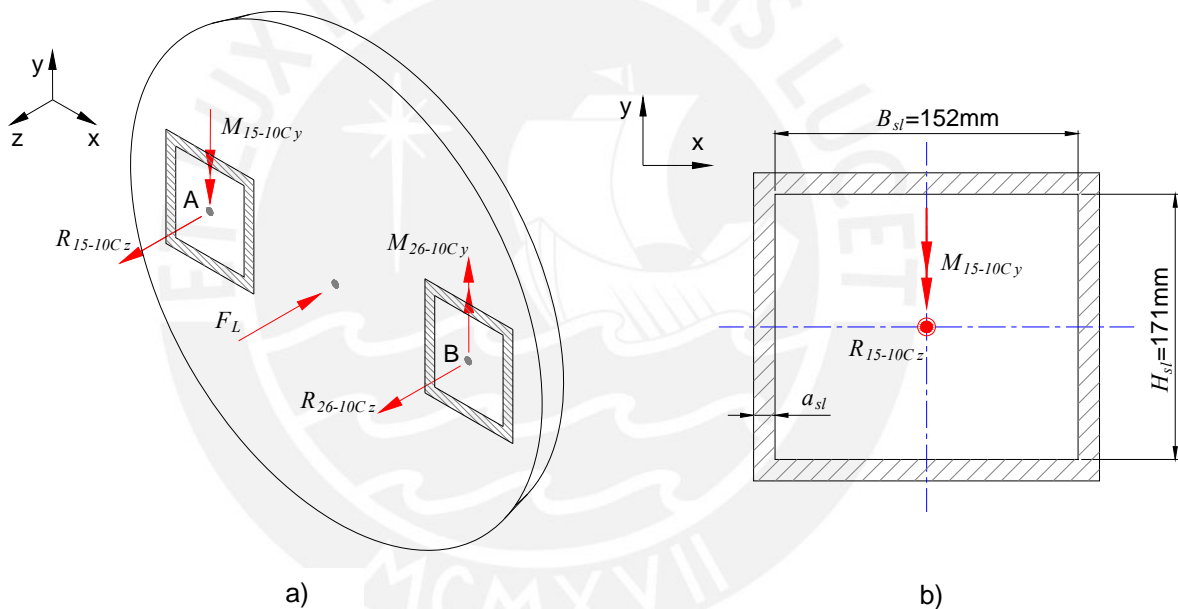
Esquema para el análisis de las soldaduras de los cubos: a) Fuerzas en los cordones. b) Cordón de soldadura en el punto A [Elaboración propia]
